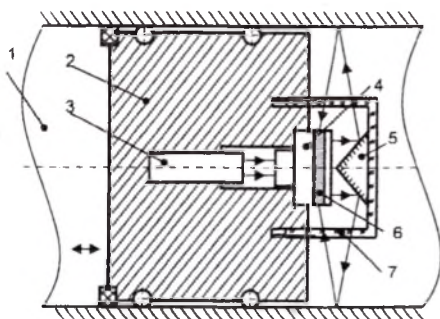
Принципиальная схема оптико-механического устройства для контроля: 1 - контролируемая поверхность, 2 - перемещаемый модуль, 3 - лазер, 4 - телескоп, 5 - коническое зеркало, 6 - кольцевая ПЗС-матрица, 7 - стеклянный стакан
